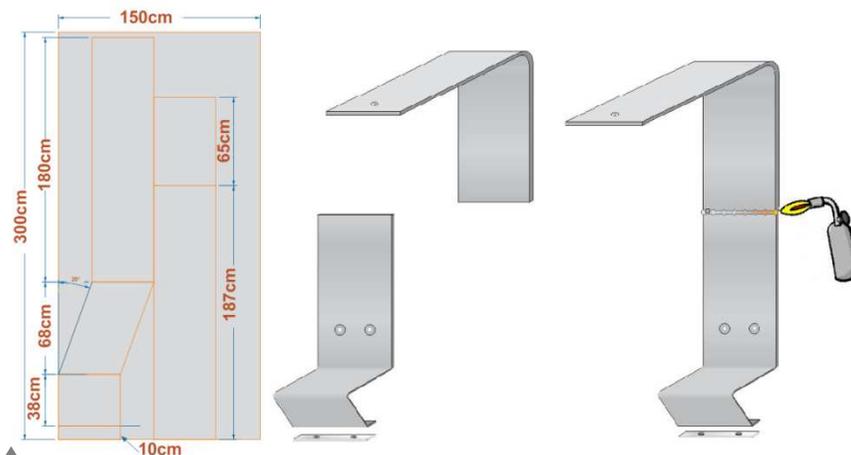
Corte do banco em chapa de aço carbono e soldagem das partes, neste caso tomando como exemplo o banco de 66cm de profundidade.
